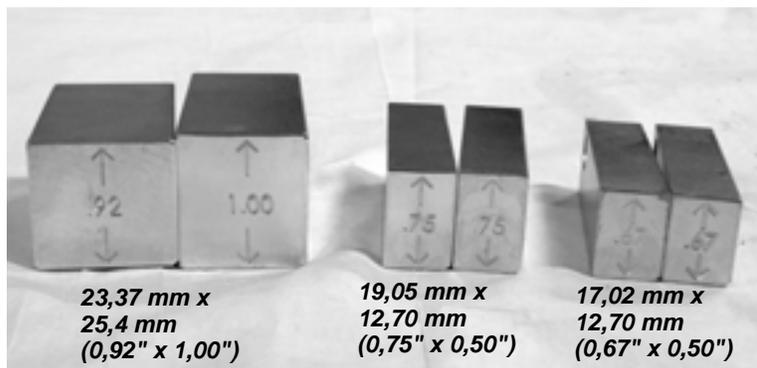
Verwenden Sie die Abstandhalter in den Werkzeughaltern, um die Werkzeugpositionen einzustellen.
